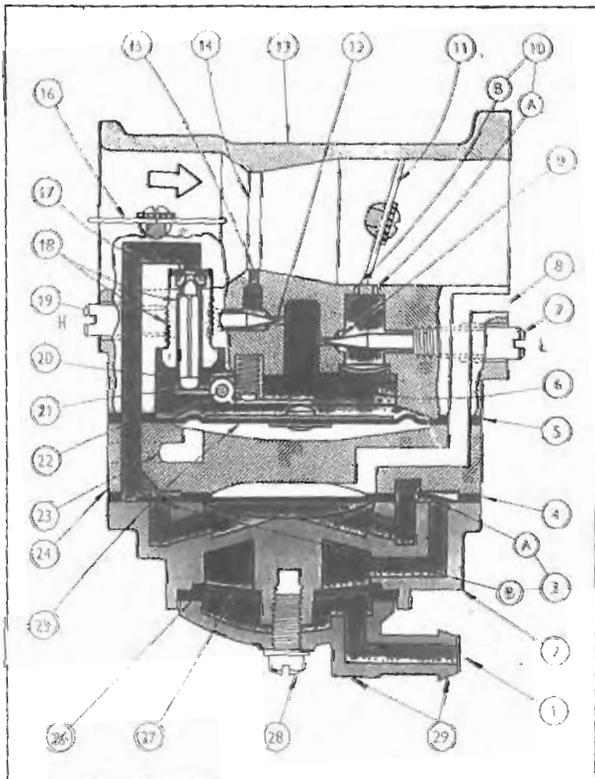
Carburador de membrana. 1.- Entrada de combustible. 2.- Cuerpo de la bomba de combustible. 3.- Membrana de la bomba: A.- Válvula de aspiración. B.- Id. de impulsión. 4 y 5.- Juntas. 6.- Caja de la membrana. 7.- Tornillo de aguja para el ajuste del surtidor de ralentí. 8.- Canal de impulsos de presión desde el cárter. 9.- Calibre de ralentí. 10.- A.- Salida primaria para combustible de ralentí (surtidor). B.- Salida secundaria de id. 11.- Mariposa de aceleración. 12.- Calibre de alta o plena carga. 13.- Cuerpo. 14.- Venturi. 15.- Surtidor principal o de plena carga. 16.- Mariposa del estrangulador de arranque. 17.- Canal de combustible. 18.- Válvula de aguja. 19.- Tornillo de aguja para el ajuste del con-
